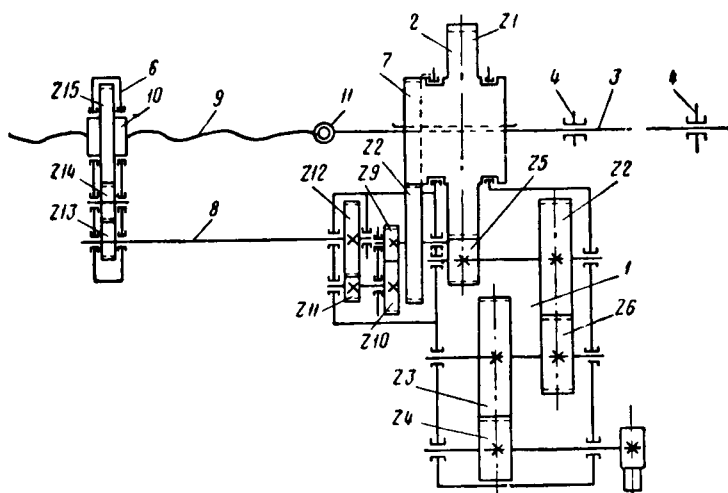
Кинематическая схема станка для расточки моторно-осевых горловин тяговых двигателей:
